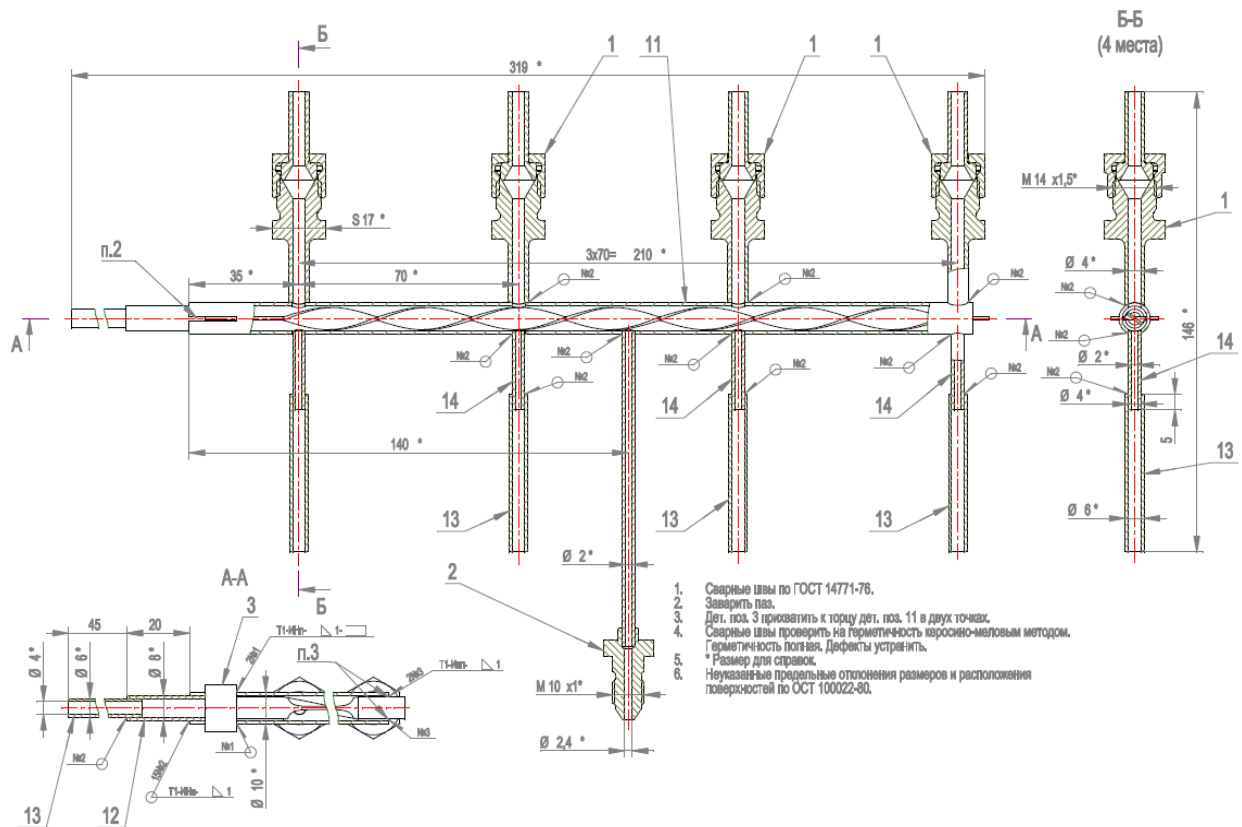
Фрагмент сборочного чертежа трубка с лентой
